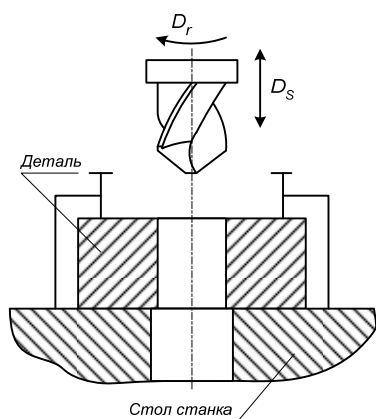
Первая схема операции сверления: обрабатываемая деталь неподвижна; сверло вращается
